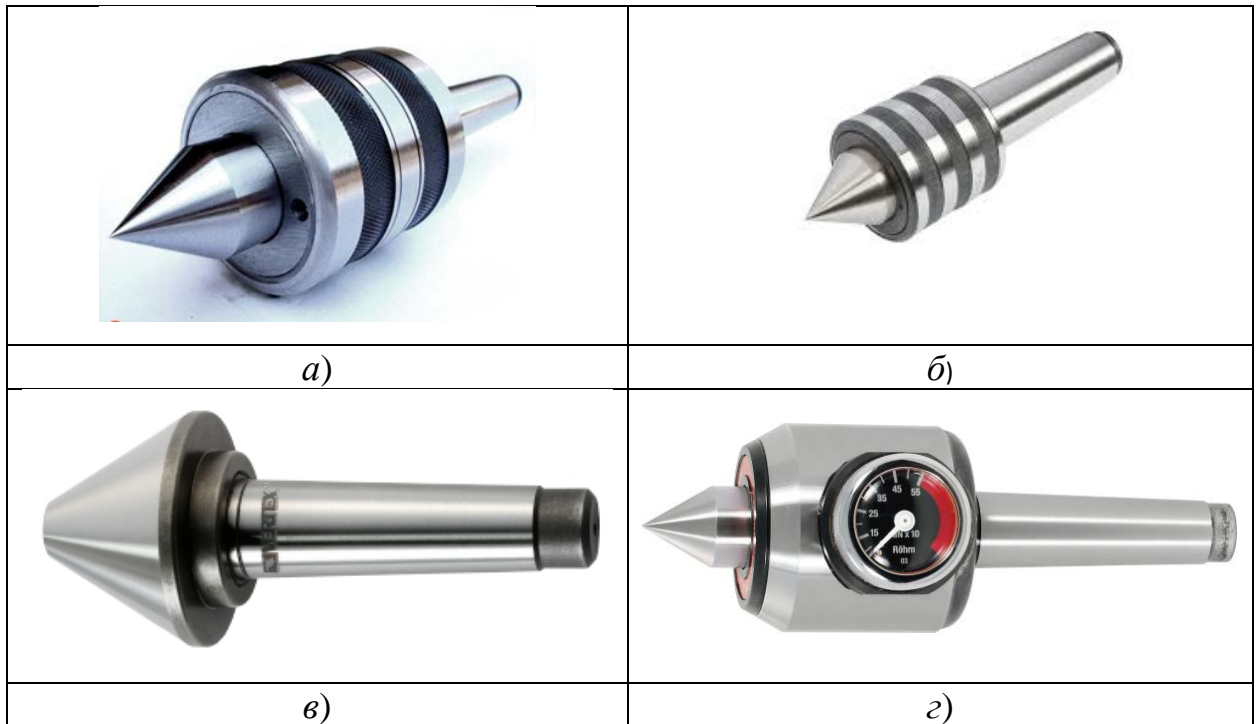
Загальний вигляд обертових задніх центрів: *а)* та *б)*-центри традиційних конструкцій для базування по конічним поверхням центрових отворів; *в)* центри для базування по внутрішніх отворах валу; *г)*-обертовий центр з визначенням реального навантаження на механізм центру.
